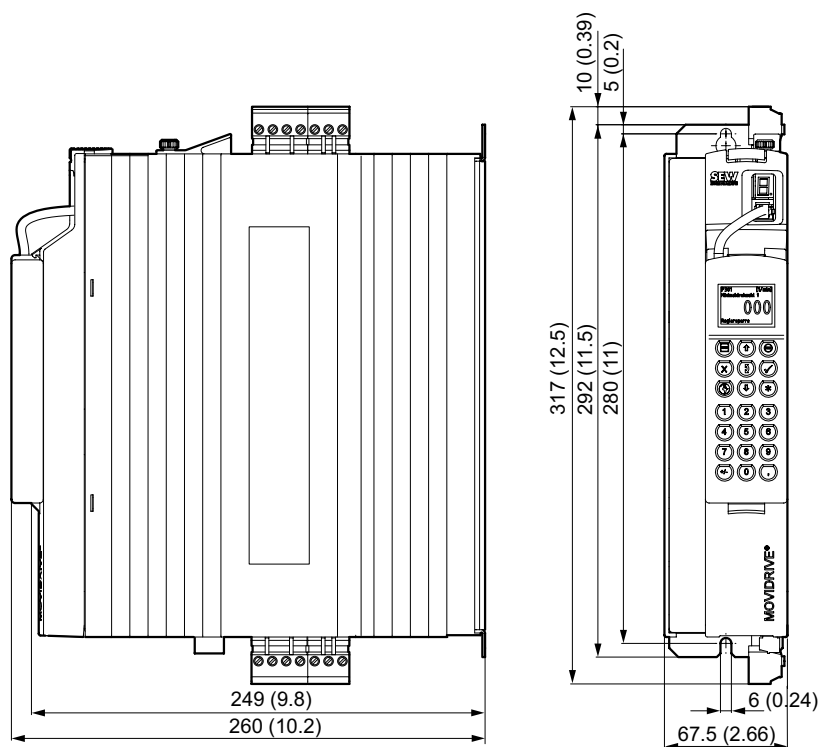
Dimensões MDX60B, tamanho 0M, dimensões em mm (in)
